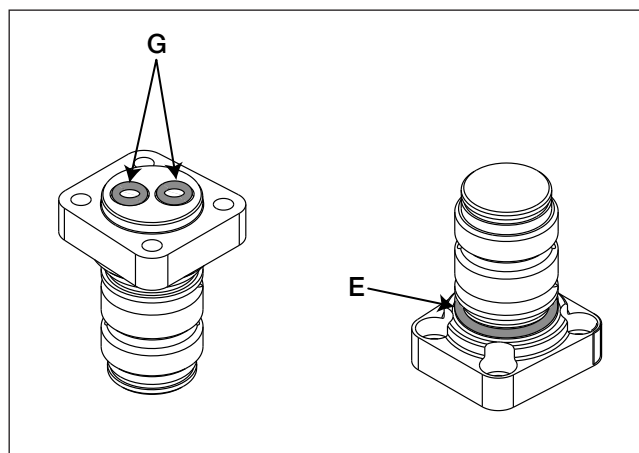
Установка уплотнительного кольца, ось шарнирного соединителя
